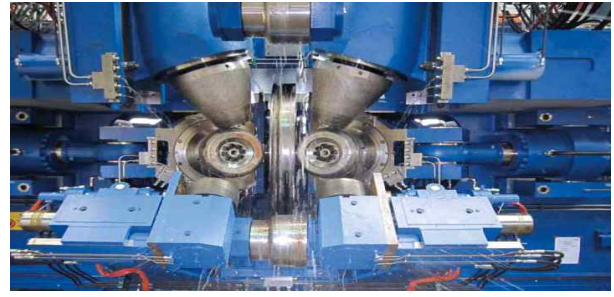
The new Schuler wheel rolling machine MHRV-180/80
